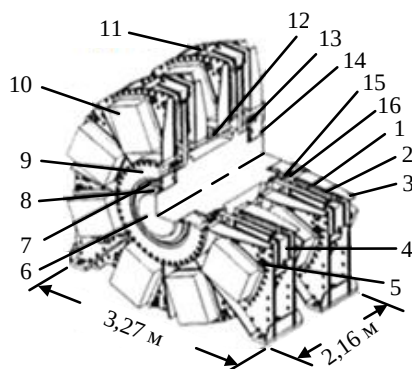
Высокогабаритный двухсторонний дисковый электродвигатель: 1 – ВПМ; 2 – статорный узел; 3 – корпус; 4 – ударный демпфер; 5 – амортизатор; 6 – вал ротора; 7 – зажим диска ротора; 8 – уплотнительный узел вала; 9 – держатель подшипника; 10 – сегмент статора; 11 – центральный каркас; 12 – распорка; 13 – диск ротора; 14 – подшипниковый узел; 15 – уплотнитель ротора; 16 – уплотнительный узел ротора
